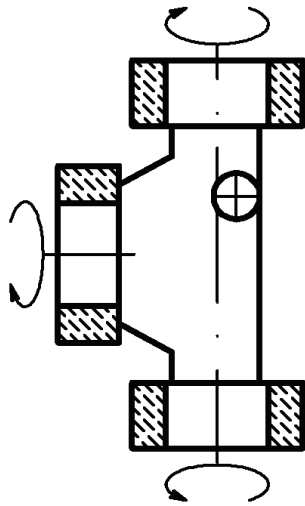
Схема способа зачистки отливок: зачистка трех плоских и цилиндрических поверхностей торцами абразивных кругов
